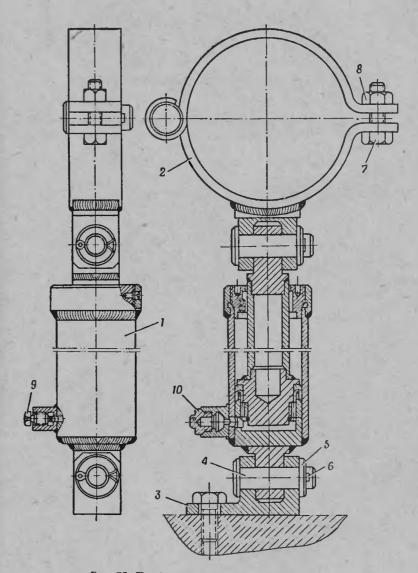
Прнбор для проверки фрикциона: 1 — динамометр; 2 — комут; 3 — кронштейн; 4 — ось; 5 — шайба; 6 — шплинт; 7 — болт; 8 — гайка; 9 — пробка; 10 — крышка
